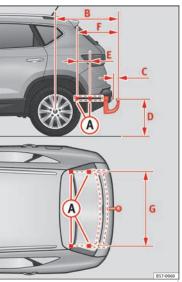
Cotes et points de fixation pour l'installation d'un dispositif d'attelage en deuxième monte.
